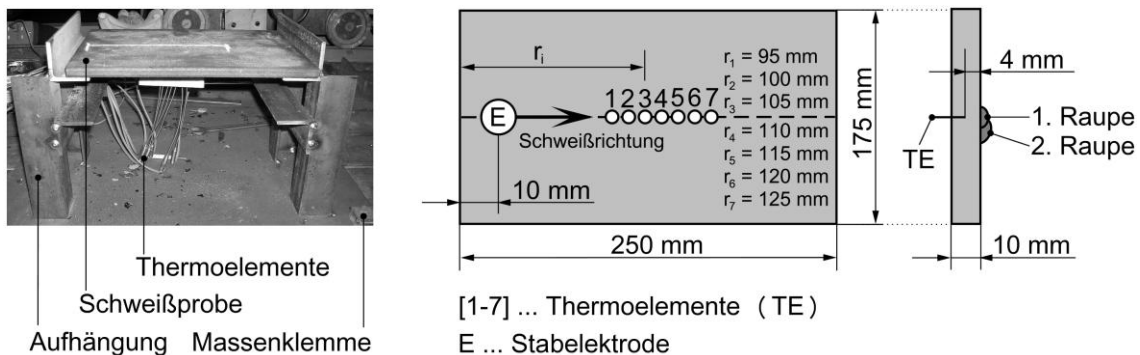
Versuchsanordnung für die E-Hand Auftragsschweißung
